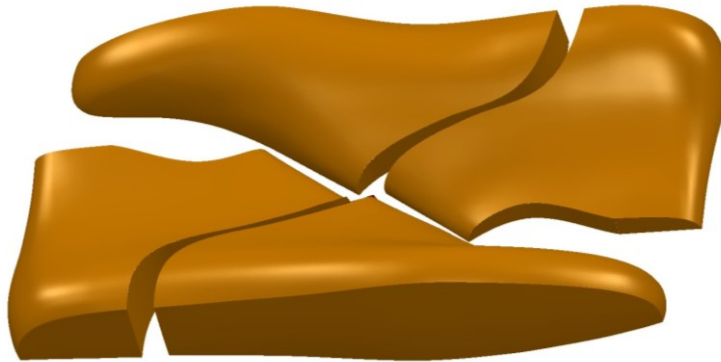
Підготовка форми колодки для фрезерування на 3-координатному верстаті з ЧПК
